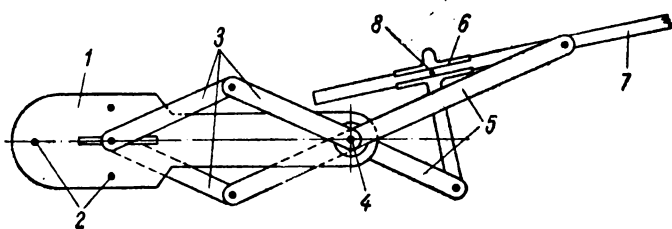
Приспособление для черчения лемнискаты Бернули.
